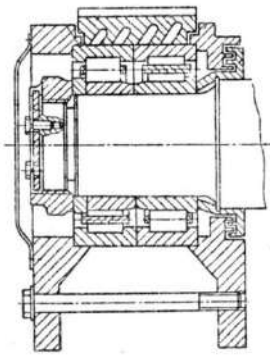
Безкорпусний буксовий вузол з проточками змінної глибини в корпусі
